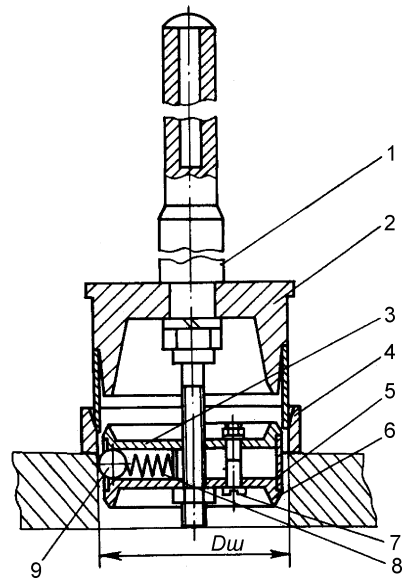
Приспособление для запрессовки свертных колец:
